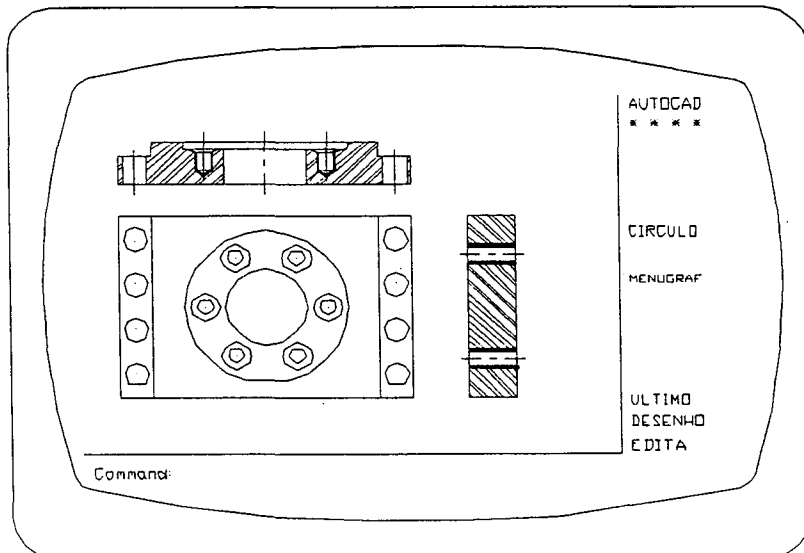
Aspecto da tela após desenho desenho da disposição de furos em círculo.
